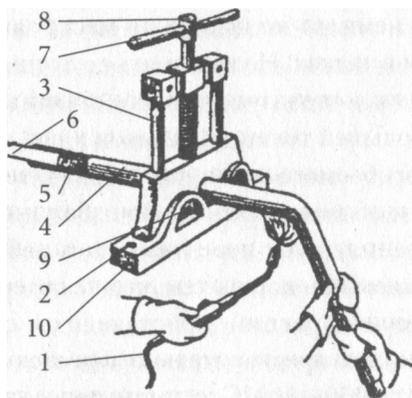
Горячее сгибание труб с помощью прижима: 1 — горелка; 2 — болт крепления прижима; 3 — колонна; 4 — изгибаемая труба; 5 — песок; 6 — пробка; 7 — рычаг; 8 — прижимной винт; 9 — призма; 10 — корпус
